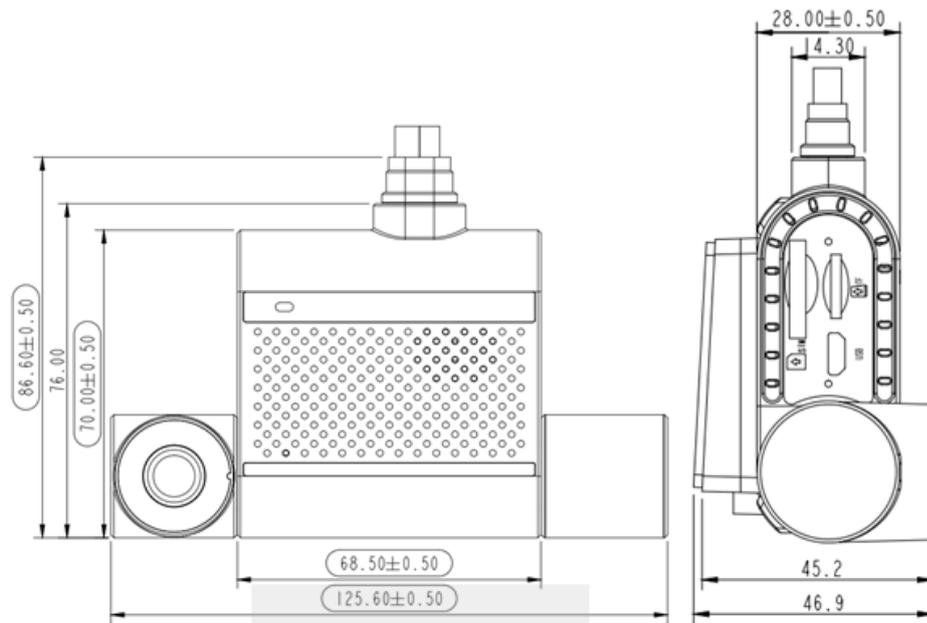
Габаритные размеры CARVIS DC-472SD
